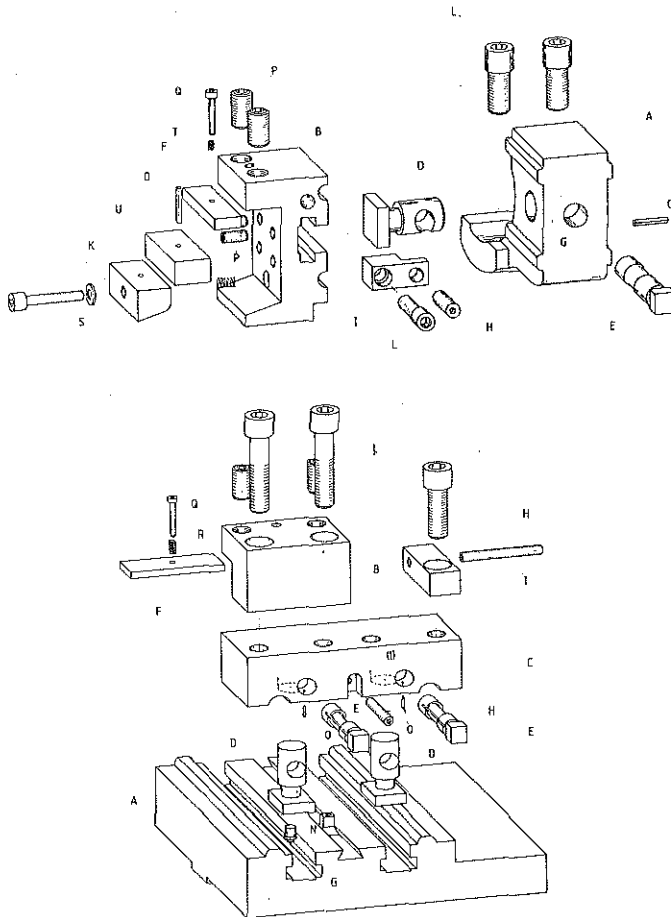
Werkzeugaufbauten aus dem Baukastensystem. Oben: Längsschlittenwerkzeug für MSA. Unten: Plan- oder Kreuzschlittenwerkzeug
